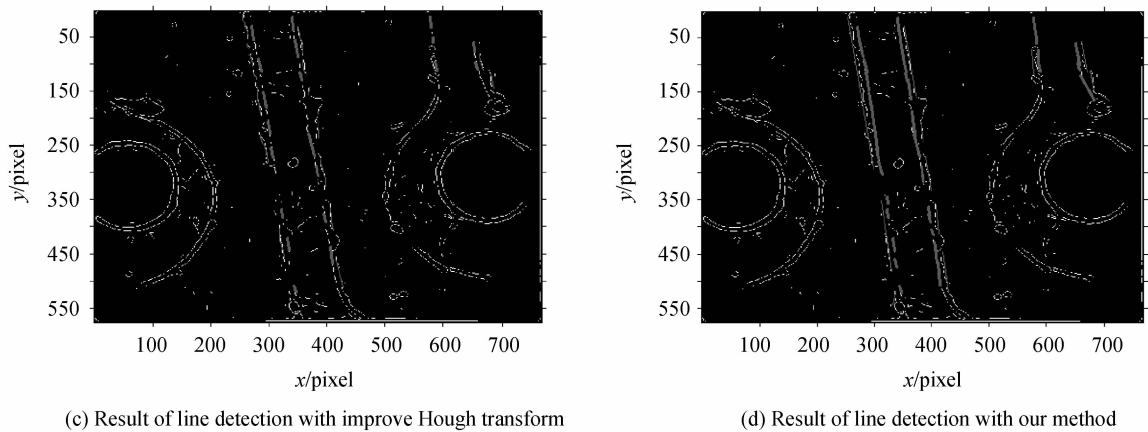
第一幅模糊且含噪声 PCB 光电图像实验结果
